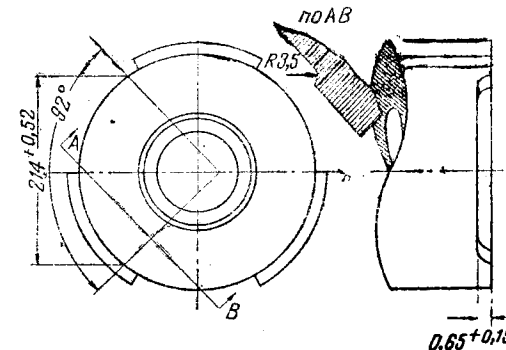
Приспособление для фрезерования концов нарезки на стволе.
